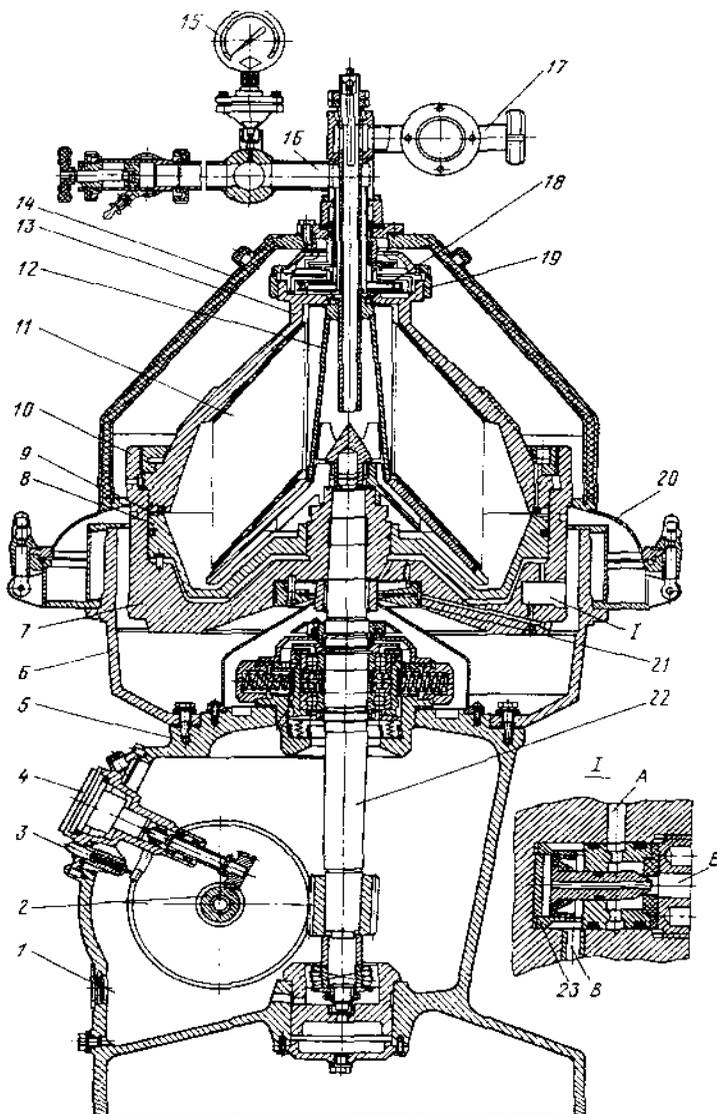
Сепаратор ВСЗ-6 (разрез общего вида): 1-смотровое окно: 2- горизонтальный вал. 3- пульсатор: 4- тахометр, 5- станина, 6 - чаша. 7 - основание, 8 - поршень 9 - разгрузочная щель, 10, 19- затяжные кольца: 11- барабан. 12 - тарелкодержатель, 13 - крышка барабана. 14 - крышка сепаратора, 15- манометр. 16 - отводной патрубков, 17 - питающая труба, 18 - напорный диск, 20 - приемник шлама, 21 – гидроузел, 22- вертикаль-
